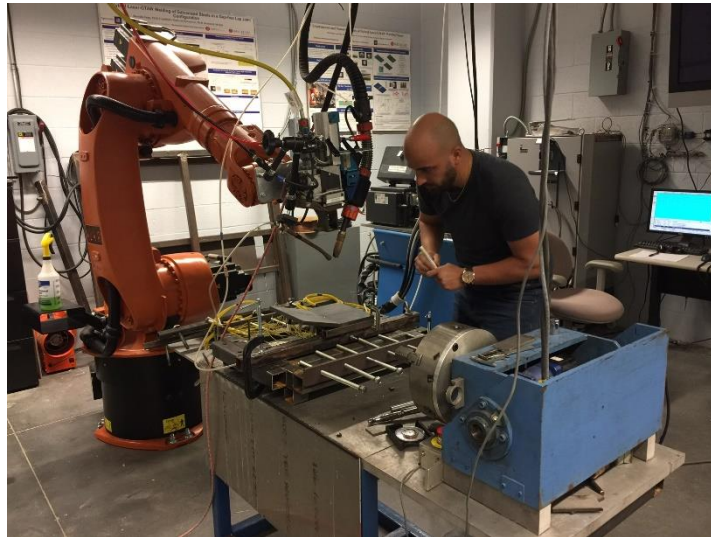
10. Equipamiento utilizado para la soldadura LBW.
